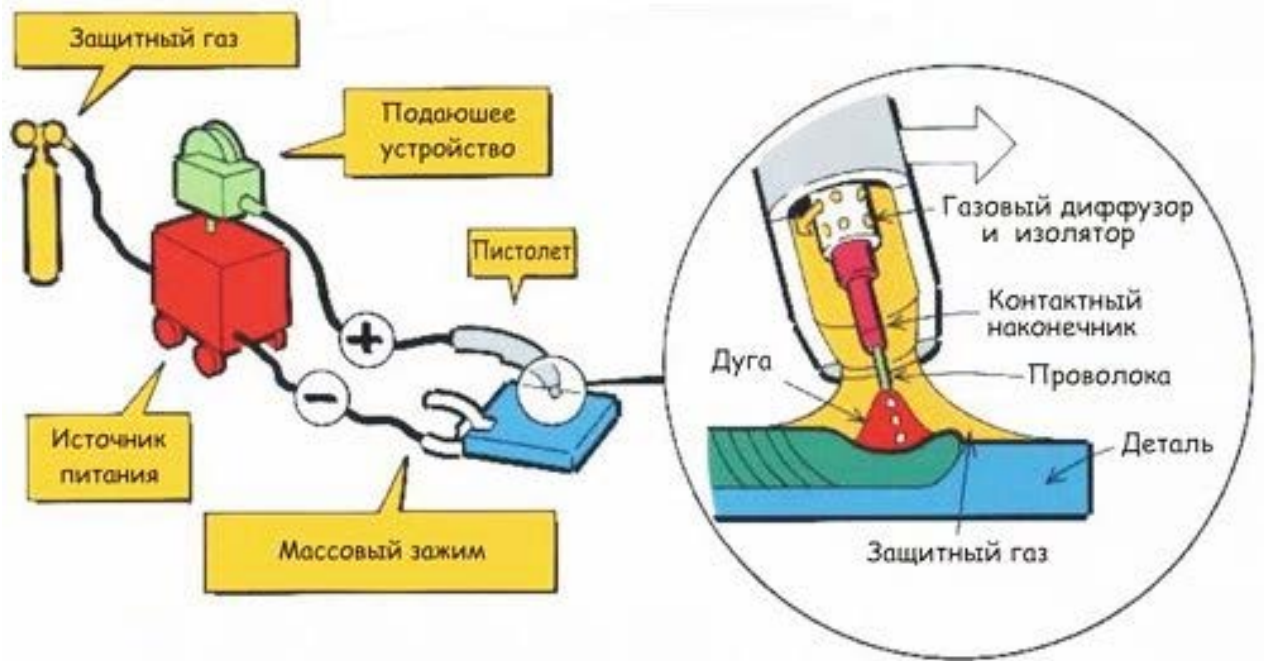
Полуавтоматическая сварка
